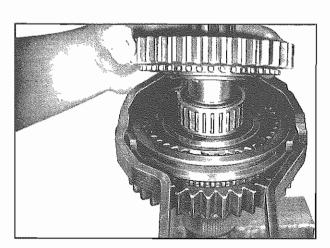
Ingranaggio della retromarcia Reverse gear wheel
